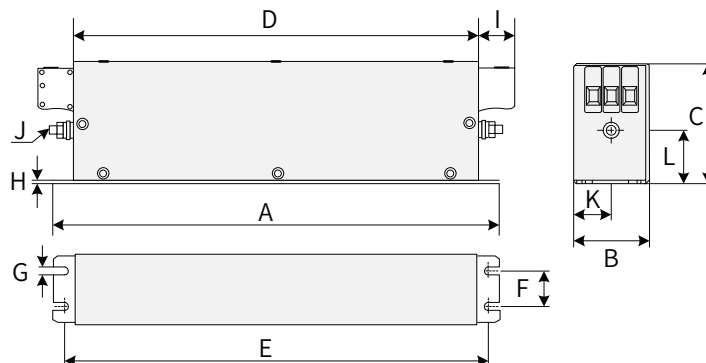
Габаритный чертеж фильтров серии FN 3258 (ед. изм.: мм)
